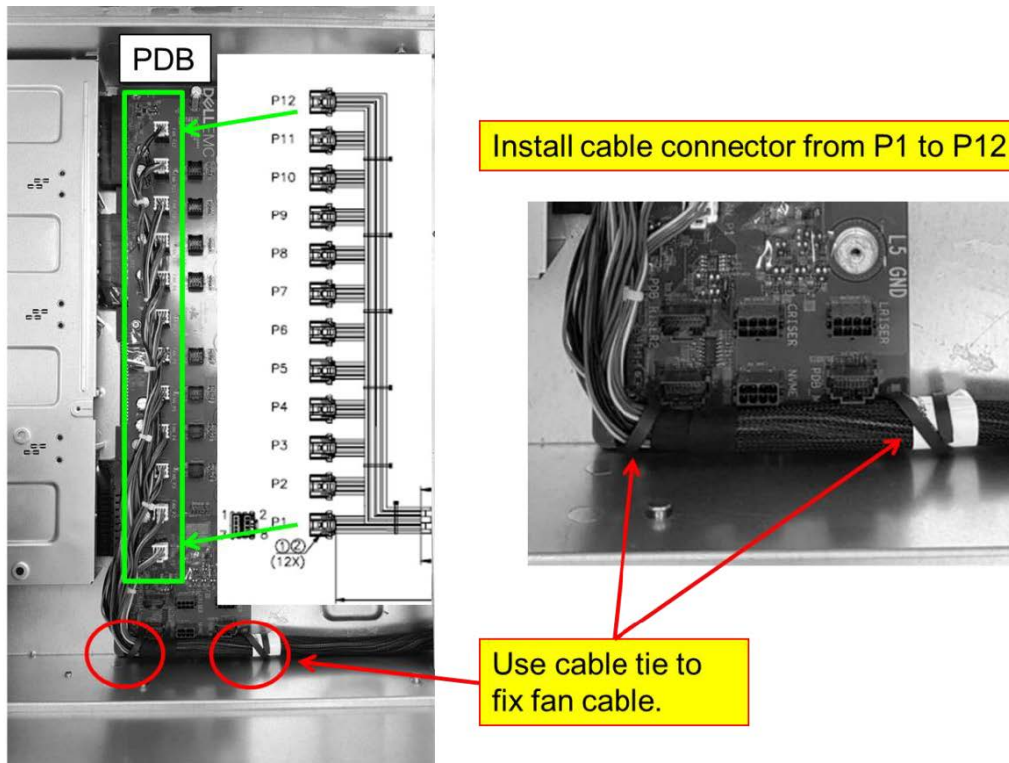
Assemblage du câble de ventilateur vers le support de ventilateur
